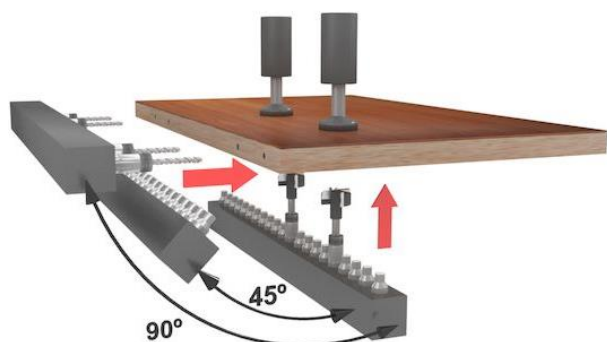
Схема обробки деталей на комбінованому багатошпиндельному свердлильно-присаджувальному верстаті
